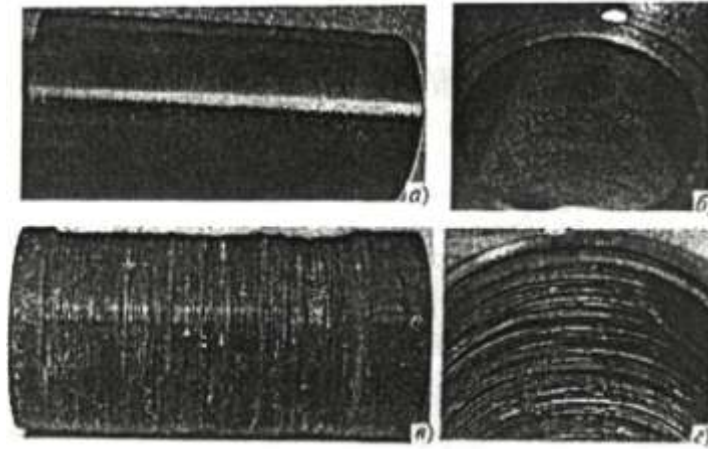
Втулки вала (а) и подшипник (б) до испытаний, наружная (в) и внутренняя (г) поверхности втулки подшипника после 950 ч работы
